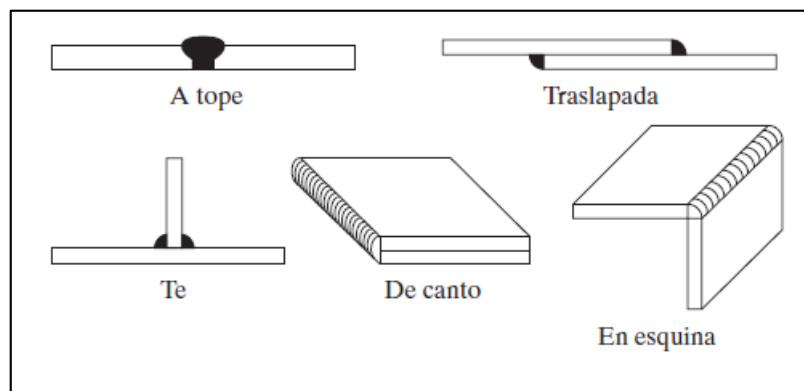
Tipos de juntas de soldadura.
